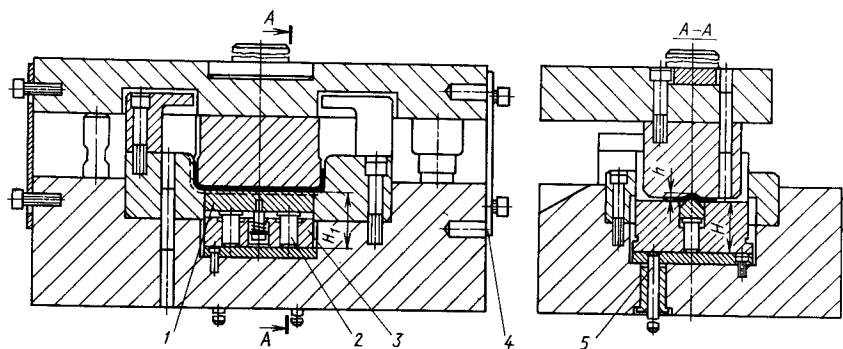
Штaмп для гибки и формовки ребра жесткости
